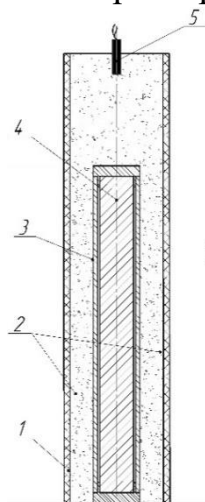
Схема сборки под сварку взрывом: 1 – опалубка, 2 – взрывчатое вещество, 3 – труба из титана ВТ1-0, 4 – стержень из меди М1, 5 – детонатор.
